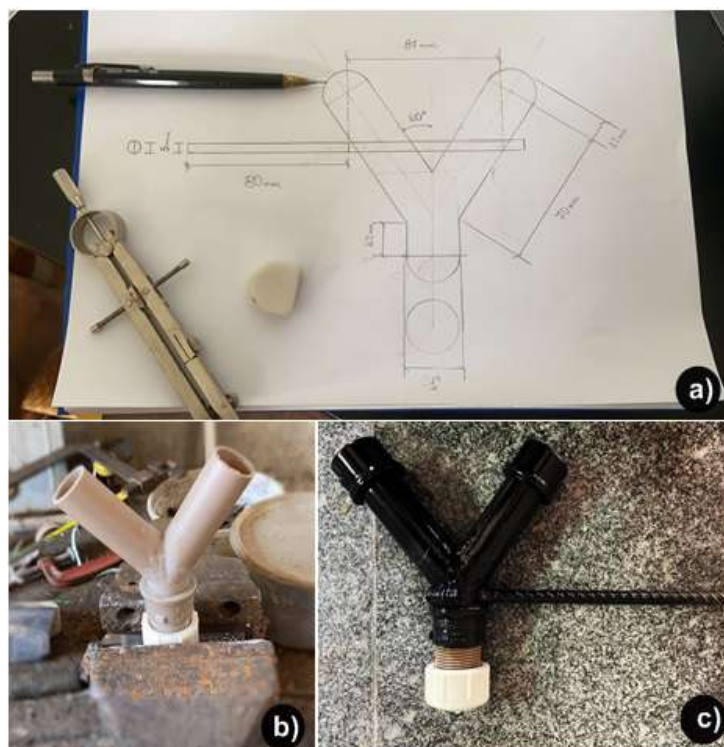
Montagem Misturador em Y: a) Desenho Técnico, b) Montagem, c) Misturador Pronto.
